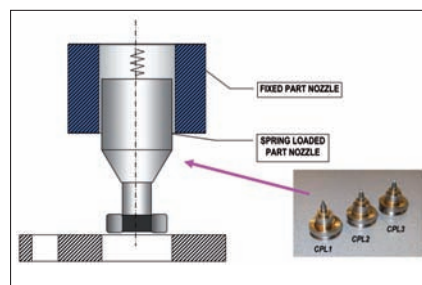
Bei den Maschinen der A-Serie werden die Komponenten mit einer gefederten Aufnahmebohrung bestückt
